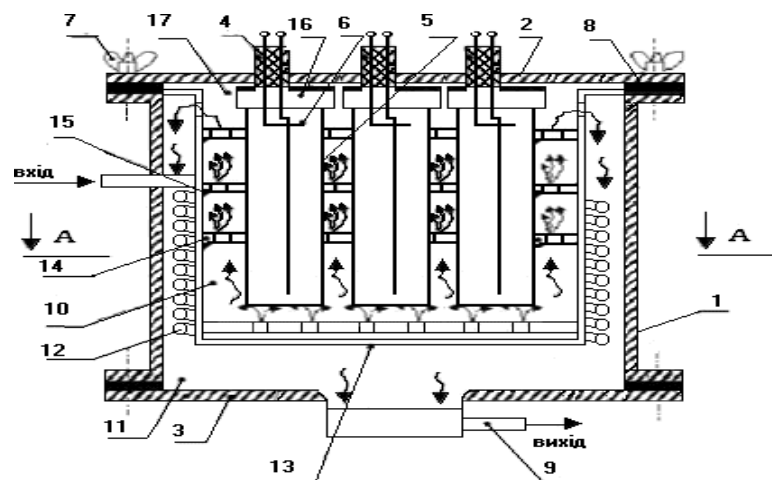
Загальний вигляд камери ІЧ-пастеризатора: 1- вертикальний корпус; 2- верхня кришка; 3- нижня кришка; 4- блок ІЧ-нагрівачів; 5- трубки; 6- ІЧ нагрівачі; 7- деталі кріплення; 8- ущільнені елементи; 9- вихідний патрубок; 10- циркуляційний насос; 11- кільцева камера; 12- зазор в камері; 13- змієвиковий теплообмінник; 14- вхідний кінець; 15, 16- штуцер; 17- дно камери; 18- отвори камери; 19- турболізатори; 20- виступи; 21- перфорований змішувач; 22- затискачі; 23 – повітряний проміжок; 24- привод синхронізатора; 25- отвори в верхній кришці.
